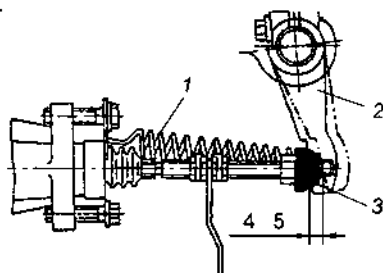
Проверка и регулировка свободного хода рычага вала вилки выключения сцепления: 1 — пружина; 2 — рычаг вала вилки выключения сцепления; 3 — сферическая гайка
